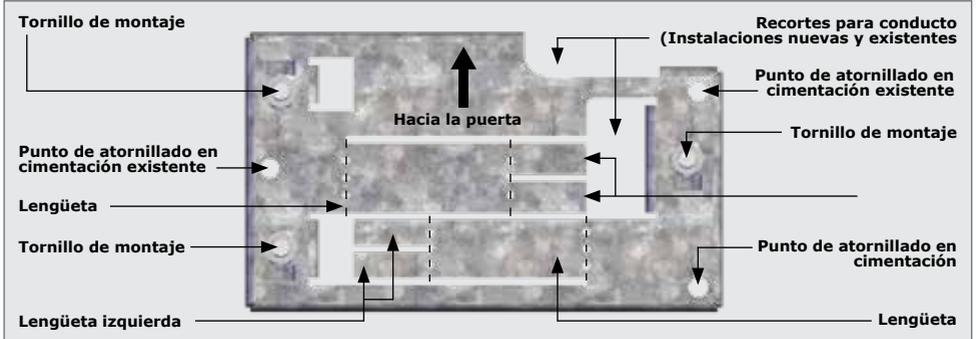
ENSAMBLE DE LA PLACA DE CIMIENTOS - VISTA SUPERIOR
